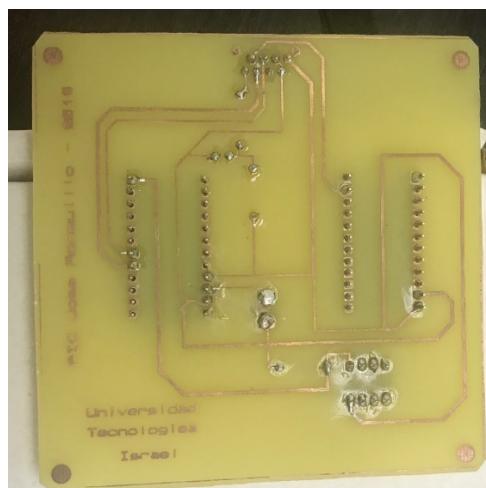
15. Placa de circuito impreso (lado cobre) con los componentes soldados
